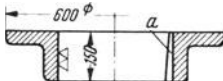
Ring (Werkzeichnung und Verkaufriß).
